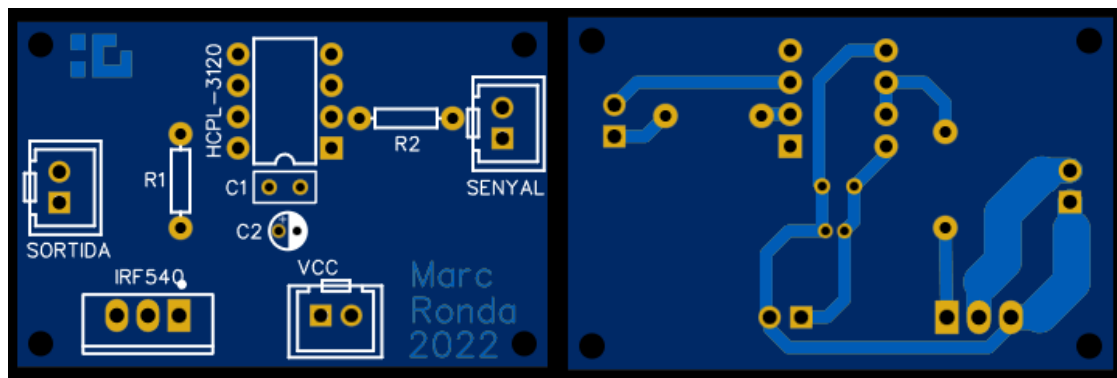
Disseny en 2D de la PCB (Disseny 5) (Font: Pròpia)
